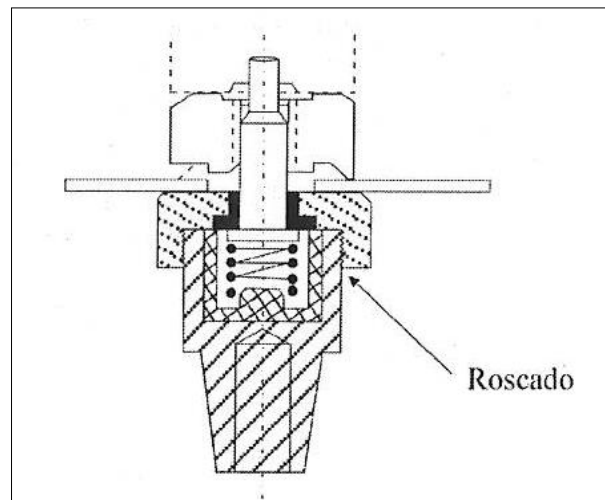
Pin centrador retráctil mediante resorte y aislado para soldadura de tuerca con cuello centrador.
